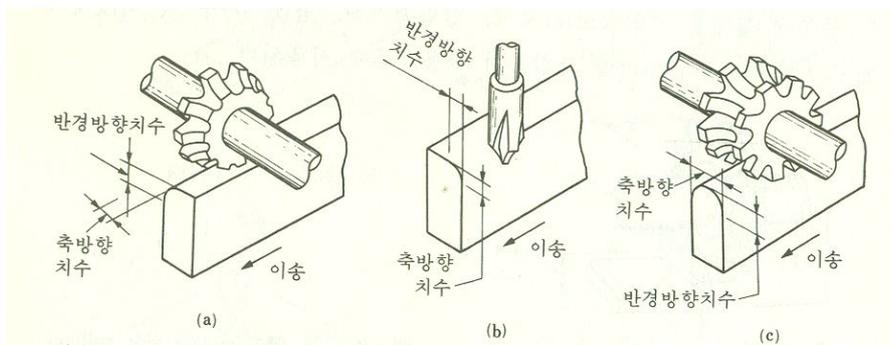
둥근 모서리 cutter(a), 둥근모서리 end mill(b), 및 오목 cutter에 의한 블록면 가공(c)
